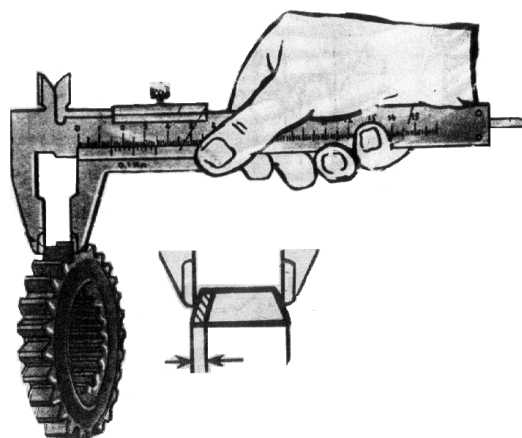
Схема измерения длины зуба штангенциркулем
